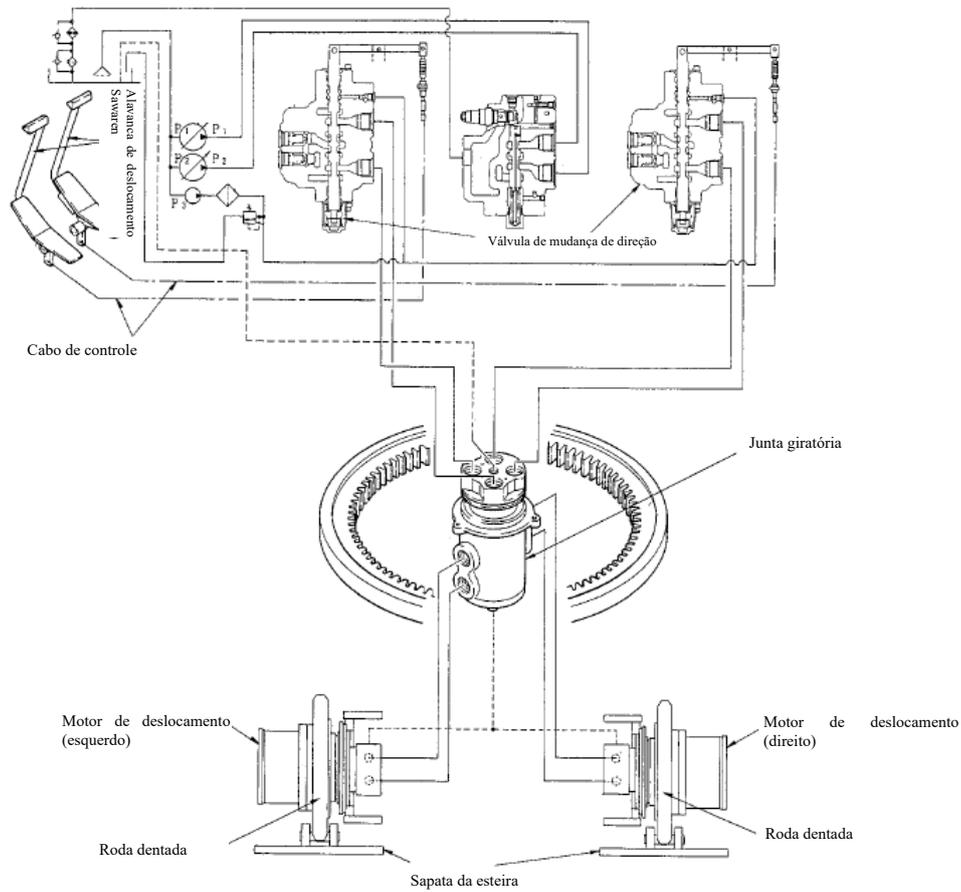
Exemplo de um circuito hidráulico para uma máquina de construção do tipo de escavadeira hidráulica
